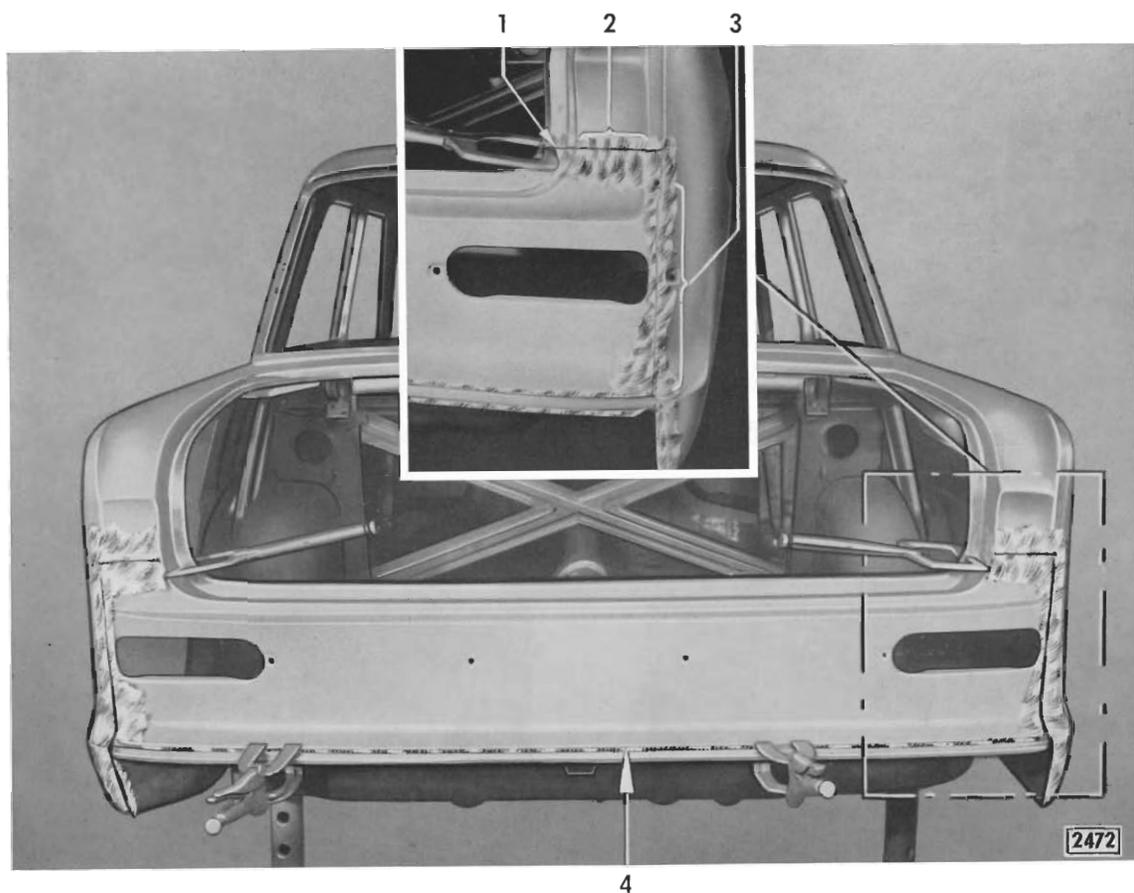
Kofferraumrückwand in Einbaulage gebracht und mit Schweißzangen festgespannt
